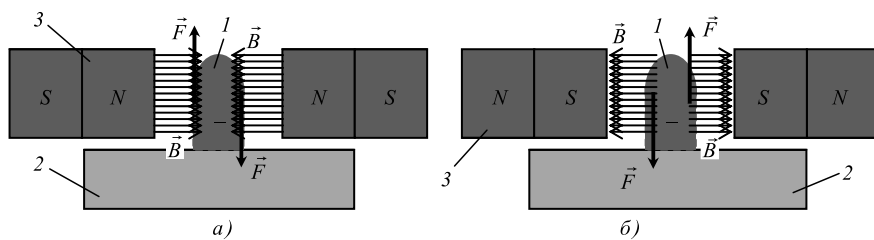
Схемы (а и б) описания передачи вращательного движения сварочной ванне:
